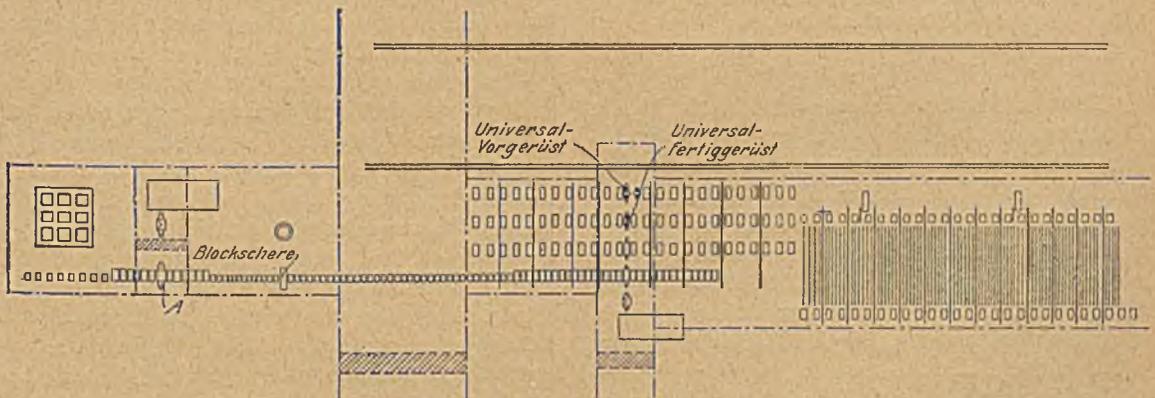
Gesamtplan einer normalen Blockstraße mit dahinterliegender normaler 950er Fertigstraße mit eingebautem Universalvor- und -fertiggerüst zur Herstellung von Breitflanschträgern mit vollkommen gleich dicken Flanschen.
